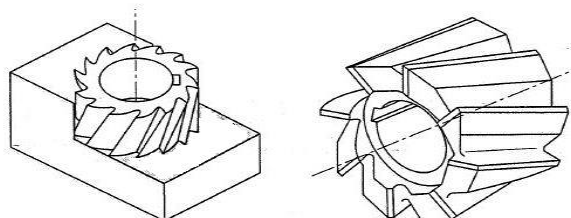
Fresa cilindrico-frontale a manicotto
